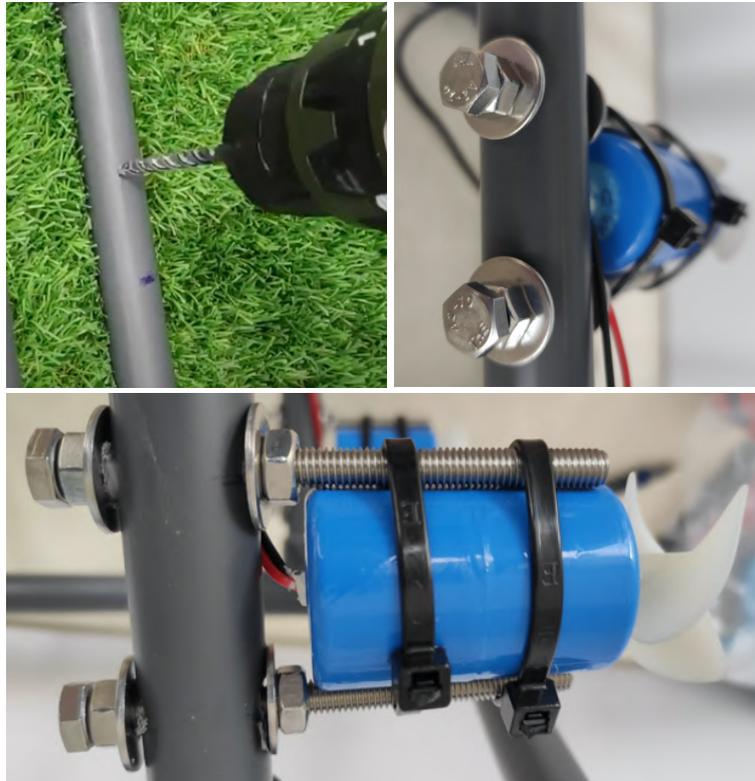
Processo de fixação dos motores ao chassi do ROV.
